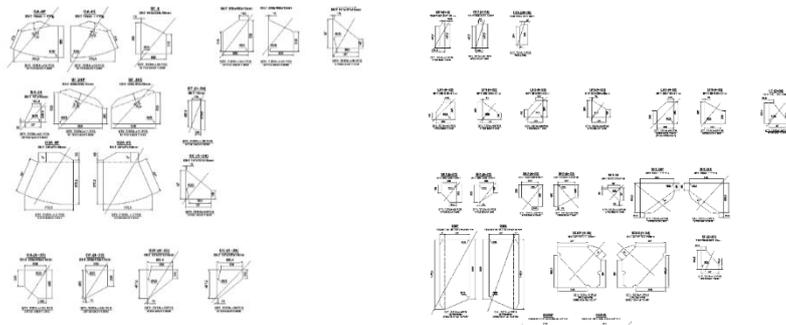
Melakukan Rutinitas *General House Keeping* dan melanjutkan Pekerjaan Cutting Plan pada Plat 12 .
